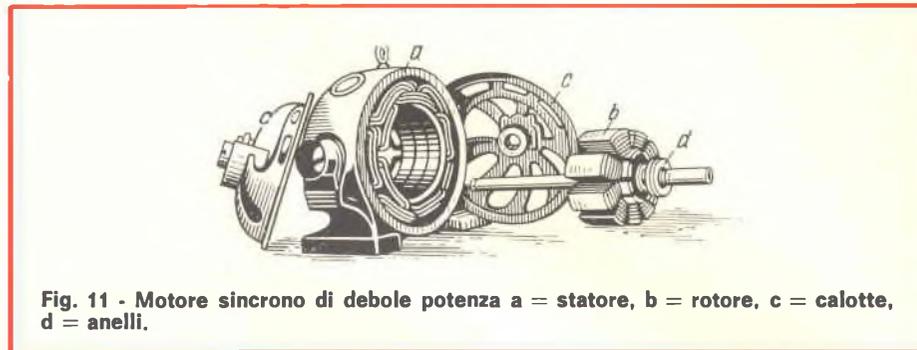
Motore sincrono di debole potenza a = statore, b = rotore, c = calotte, d = anelli.
